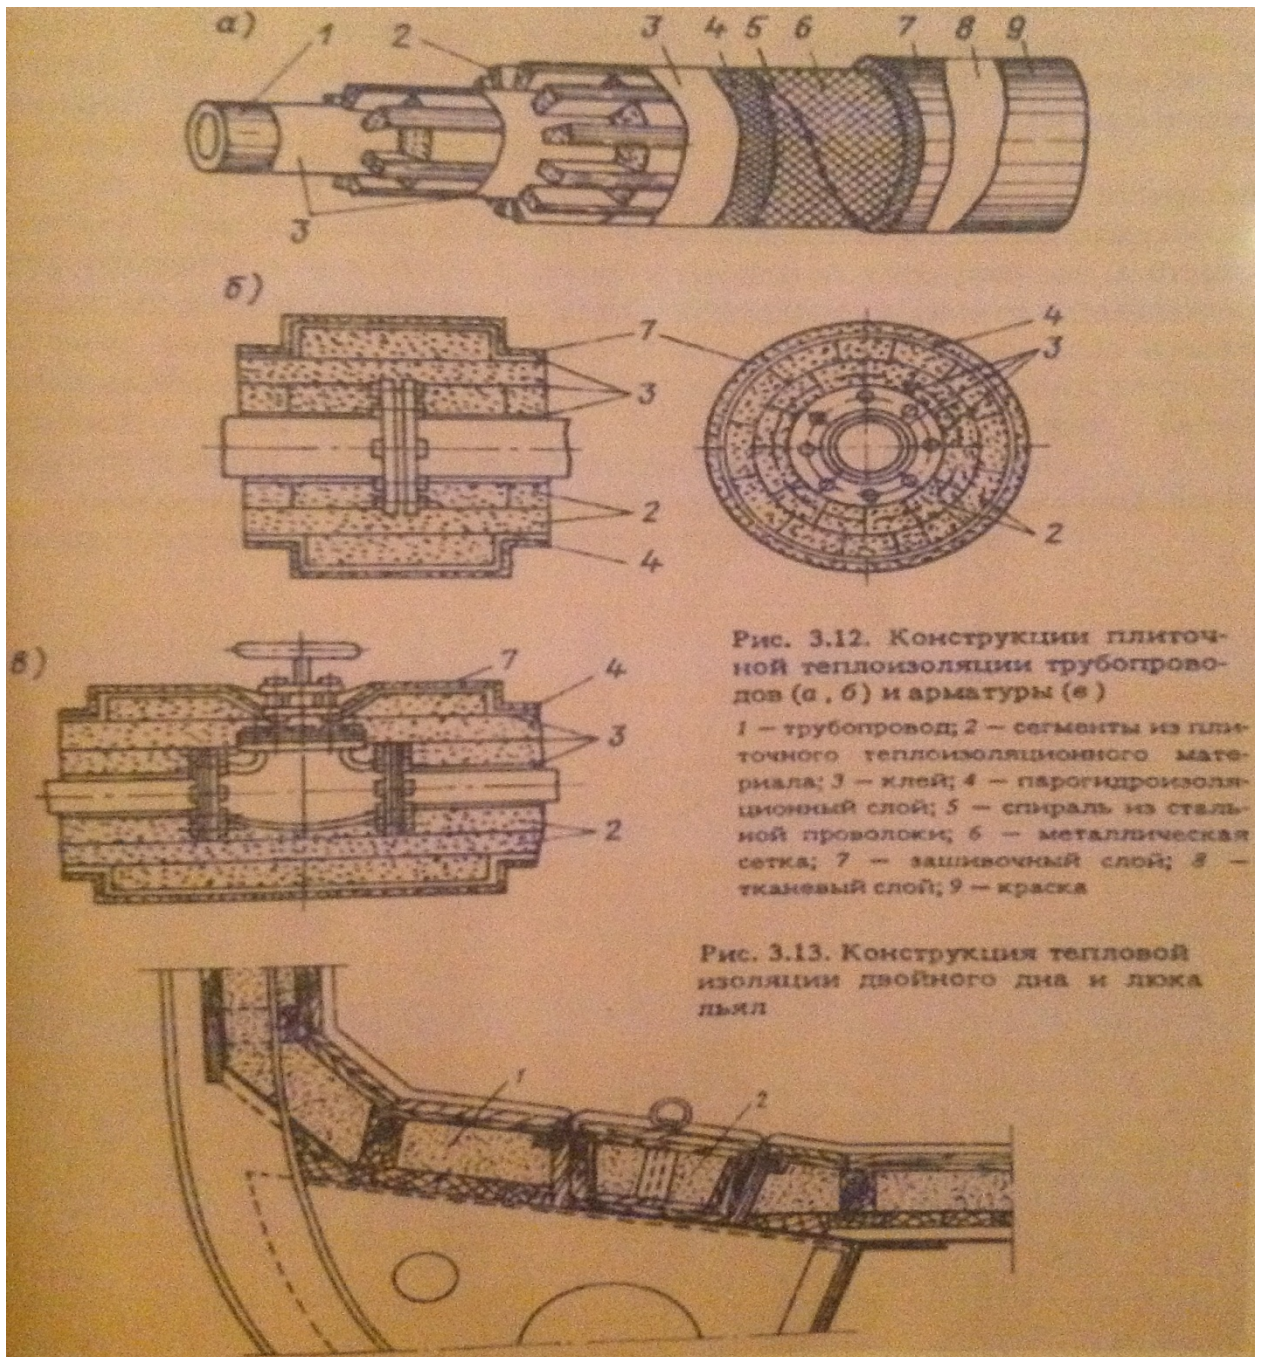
Конструкции плиточной теплоизоляции трубопроводов (а, б) и арматуры (в)
